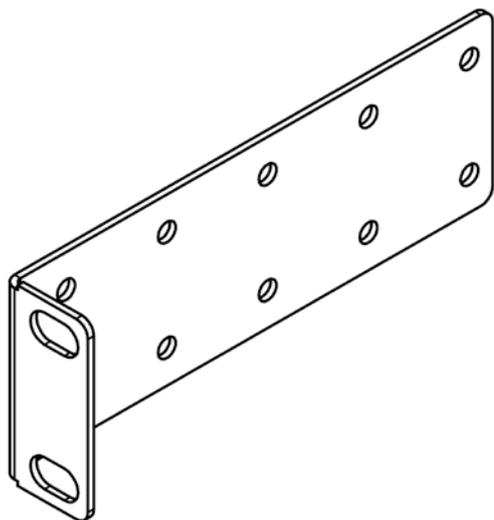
Дополнительная скоба для крепления к стойке.
